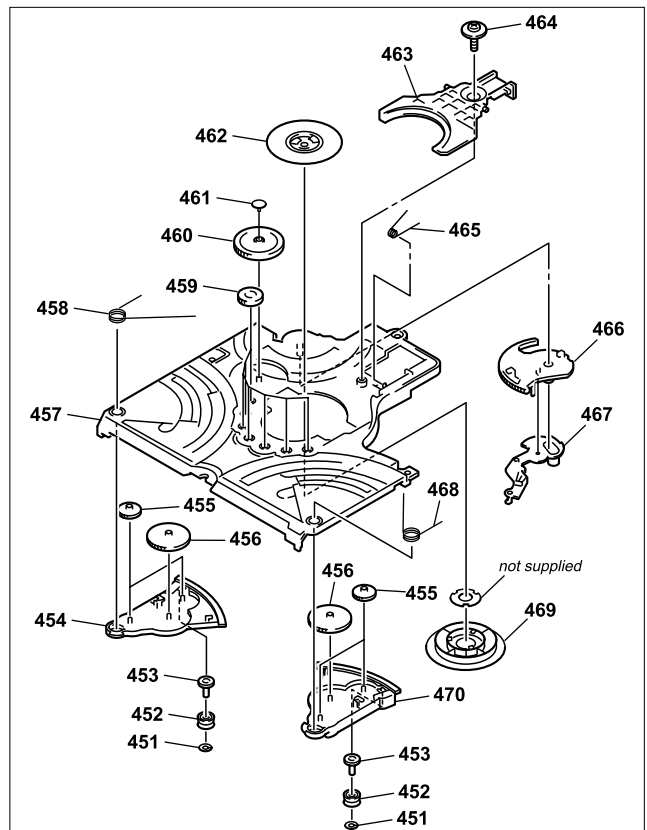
Сборочный чертеж механизма CDM80-DVBU24 (секция 2)
